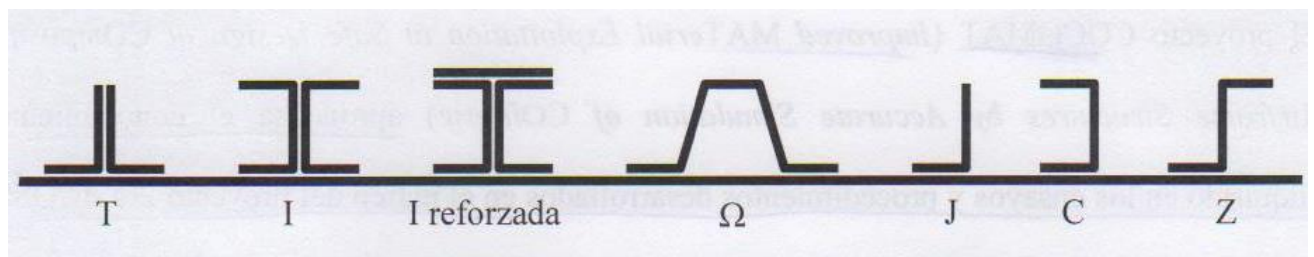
Tipos de secciones transversales típicas de los rigidizadores (reproducida con autorización de J. Reinoso [4])
